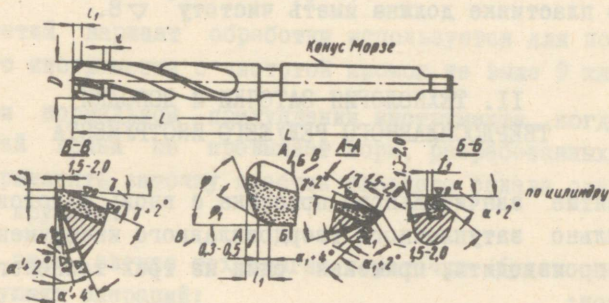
Углы заточки твердосплавного зенкера под алмазную обработку.
